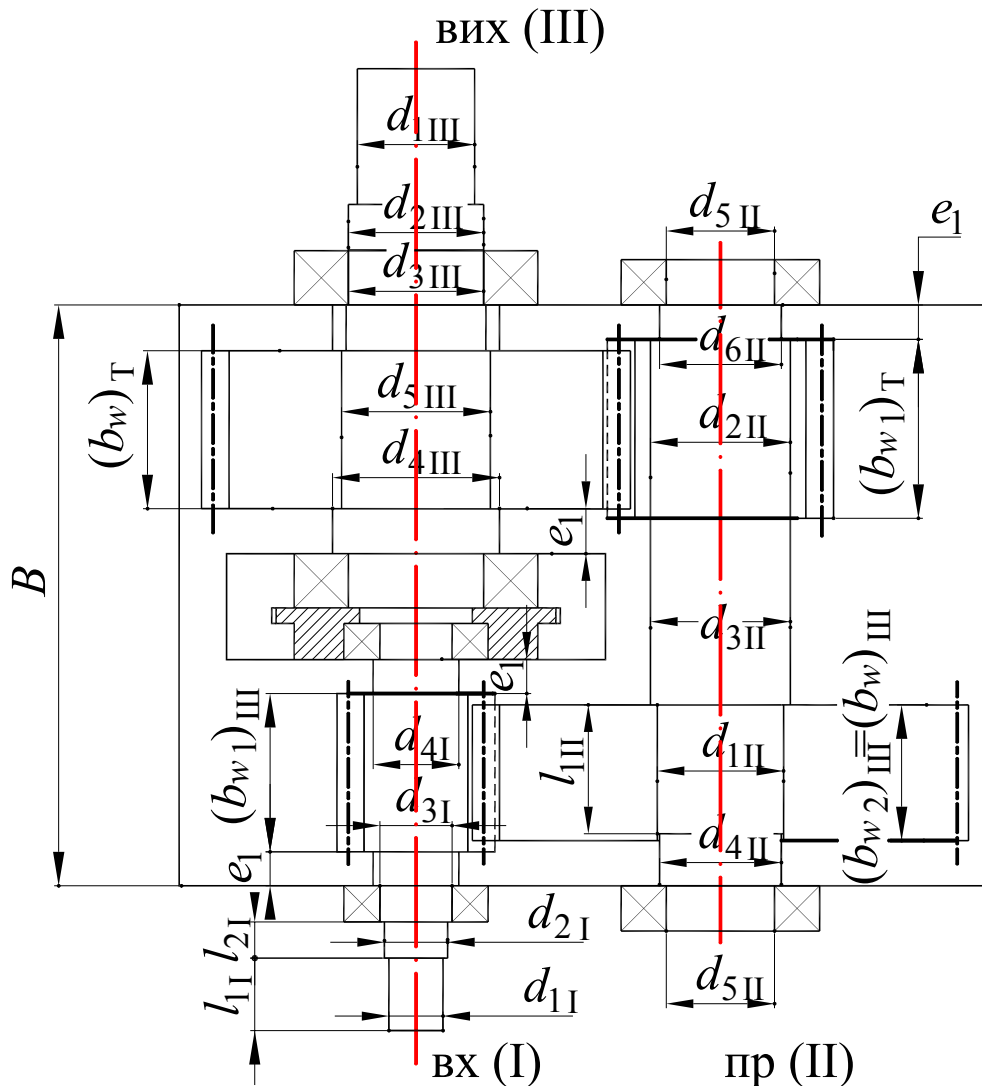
Другий етап ескізного компоунвання редуктора за співвісною схемою
